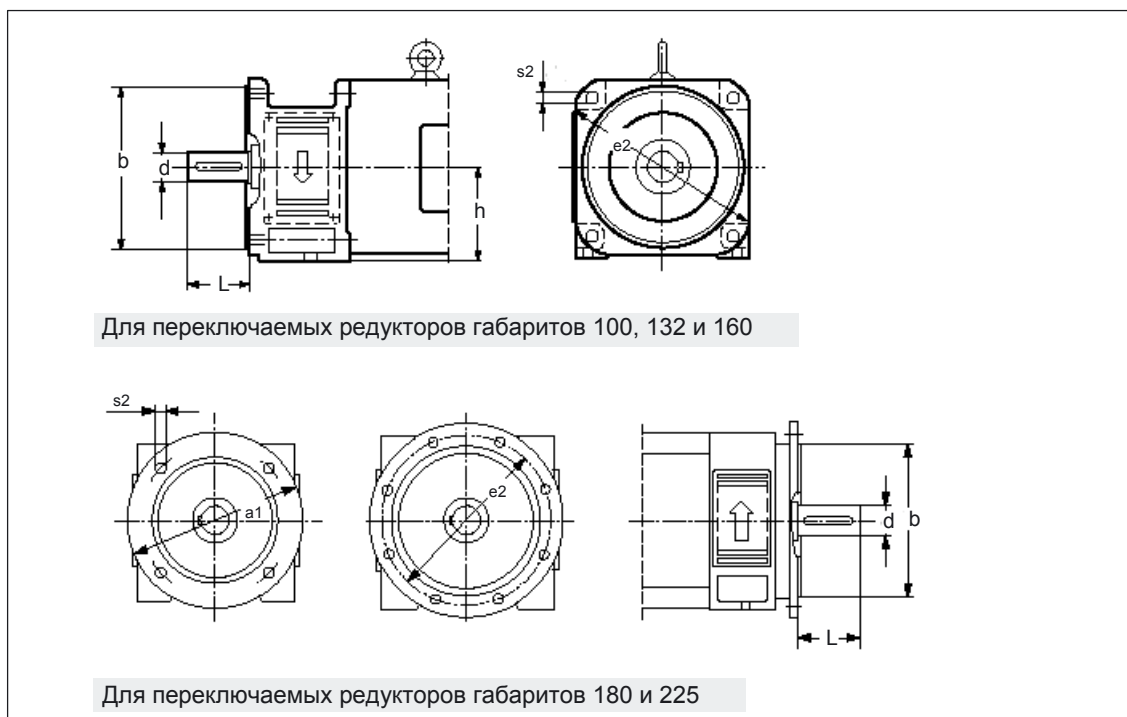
Размеры фланца для двигателя трехфазного тока
